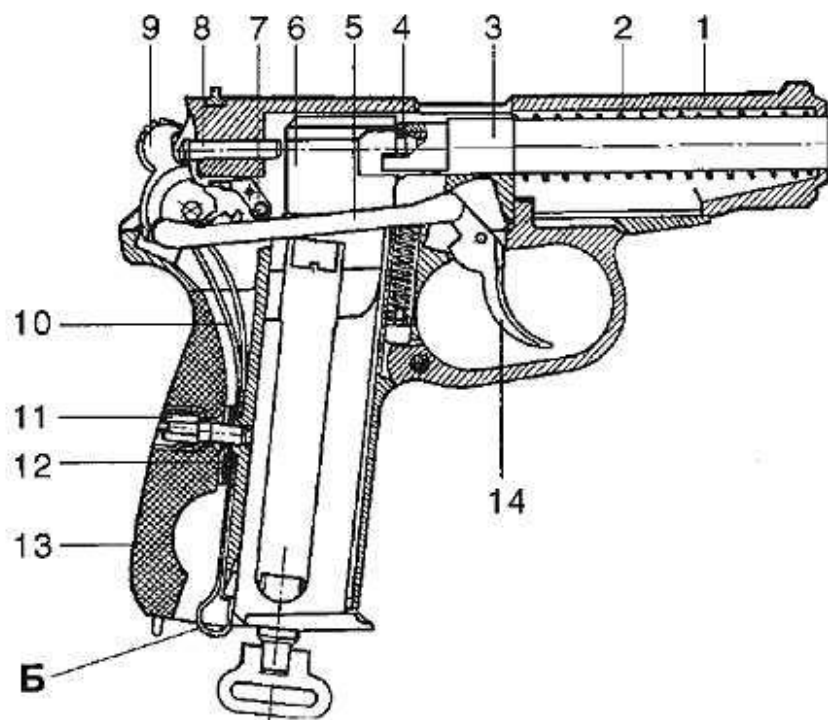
Схема пистолета МР-654К: 1 — затвор; 2 — пружина возвратная; 3 — рамка со стволом; 4 — прокладка ствола; 5 — тяга с рычагом взвода; 6 — магазин; 7 — шептало; 8 — ударник; 9 — курок; 10 — пружина боевая; 11 — винт рукоятки; 12 — задвижка; 13 — рукоятка; 14 — крючок спусковой; Б — защелка магазина
